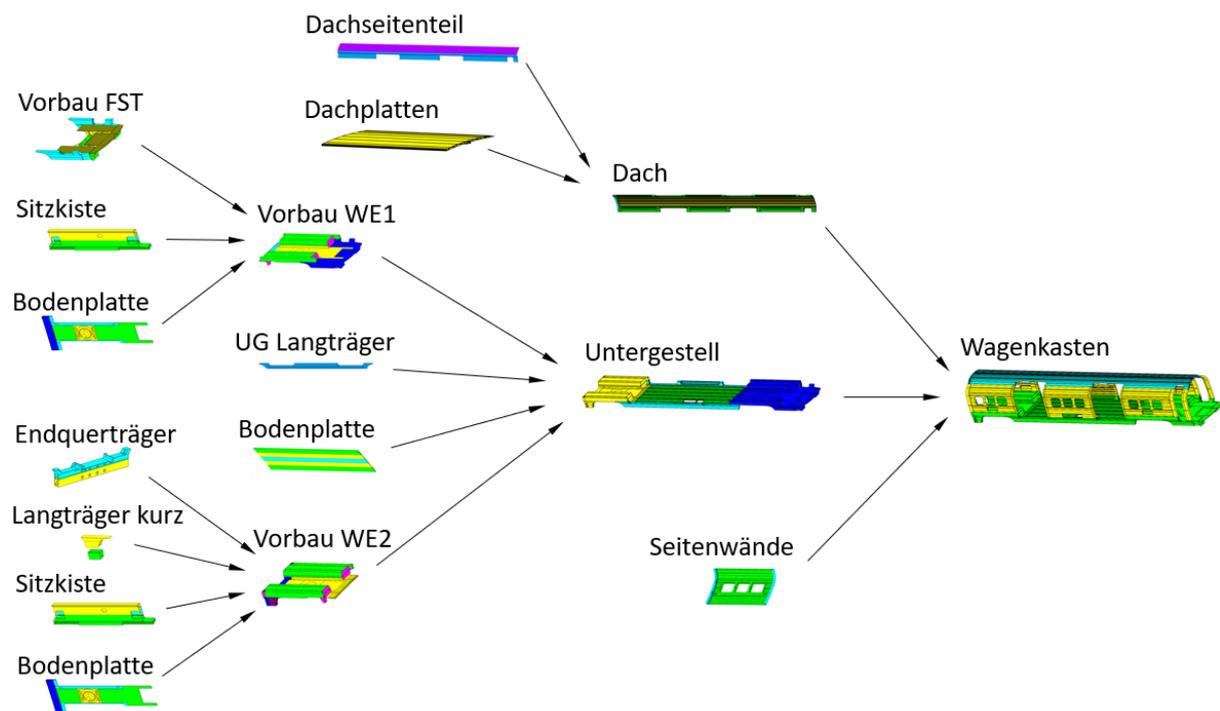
Wagenkastenstruktur Haupt- und Unterbaugruppen
